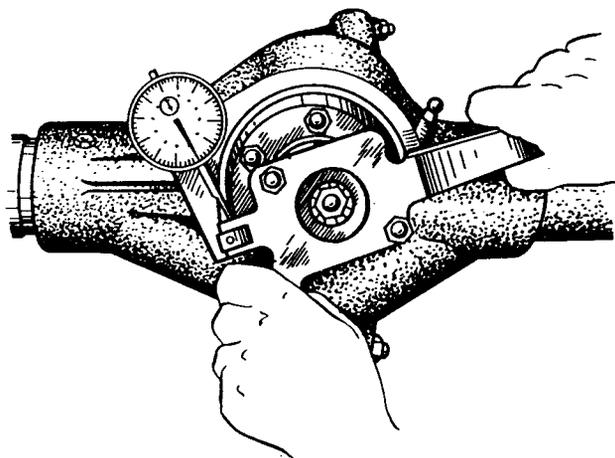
Prüfung des Flankenspiels in der Verzahnung der Haupttrieberräder
